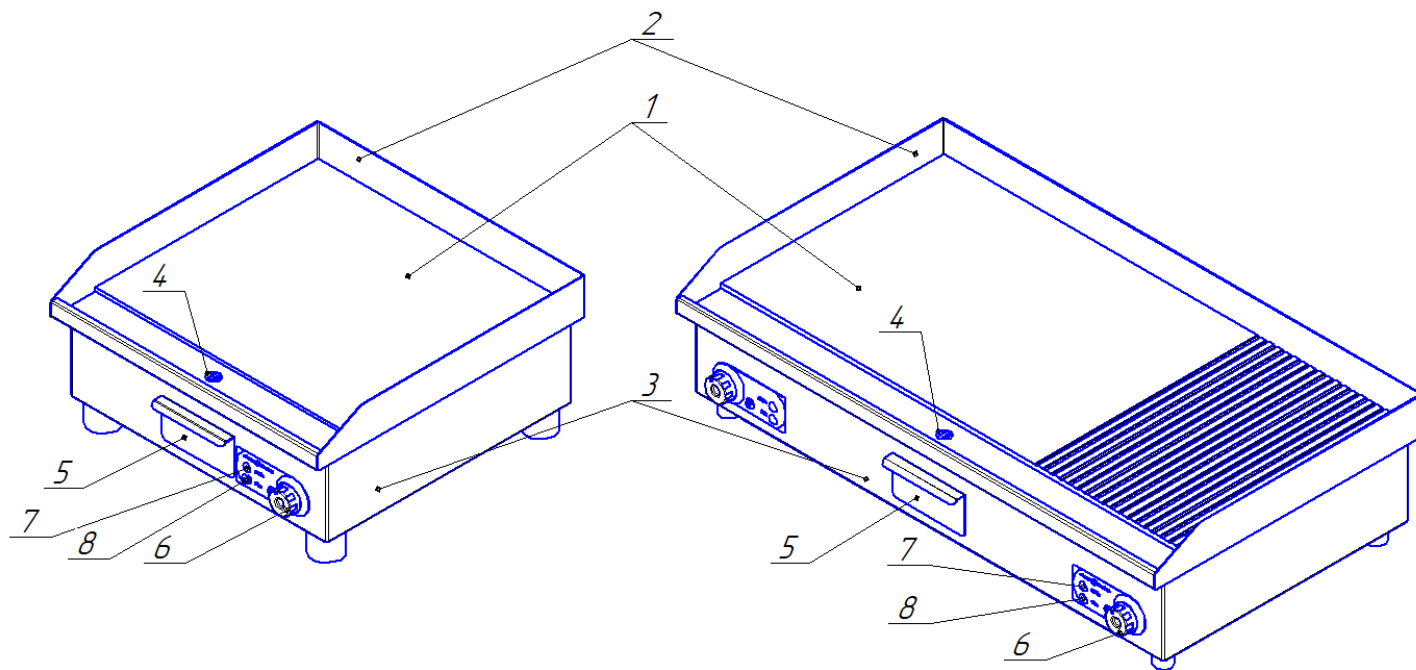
Общий вид поверхность жарочная ПЖ и ПЖ-К.
